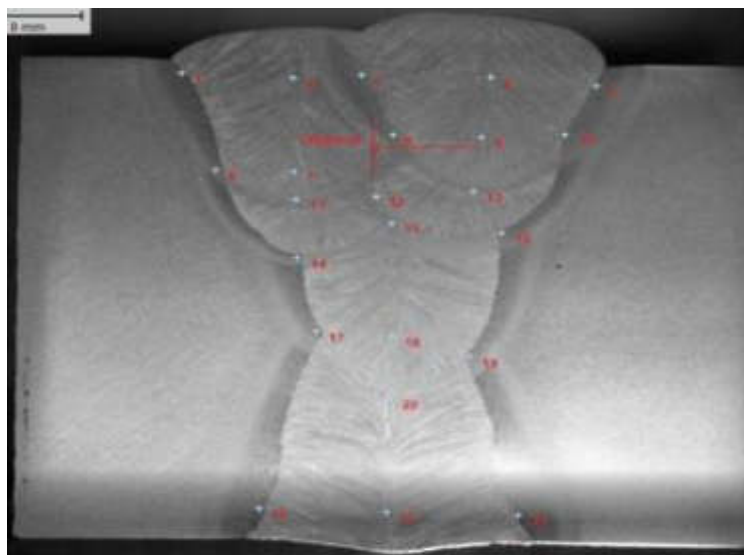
Шлиф после сварки с применением двух дуг
